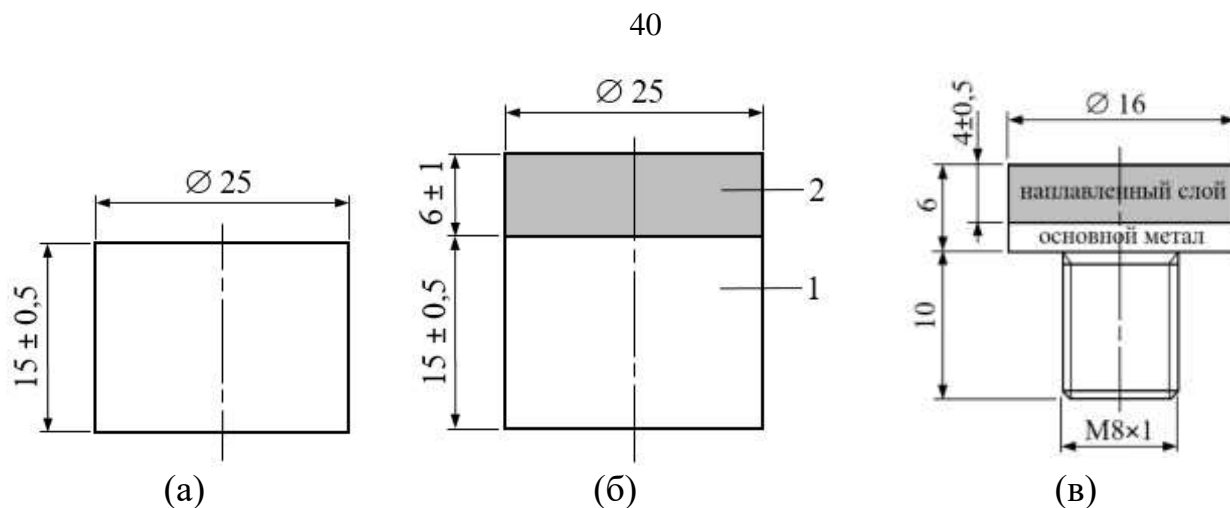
Подготовка образца наплавкой методами РДС и TIG: а – основной металл (подложка), б – основной металл с наплавленным слоем (ППМ-6, E308L-17, 06X19H9T), в – образец с основным металлом и наплавкой
